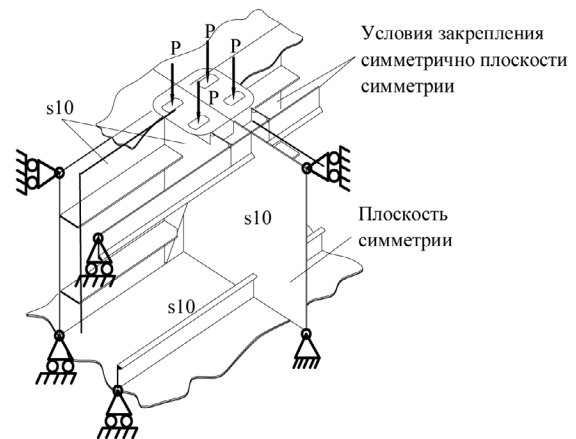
Расчетная схема подкрепления контейнерного фитинга днищевых корпусных конструкций
